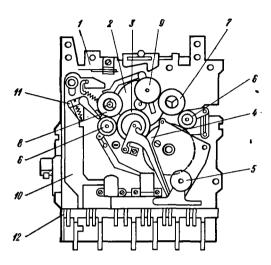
Внешний вид ЛПМ (вид сверху):
